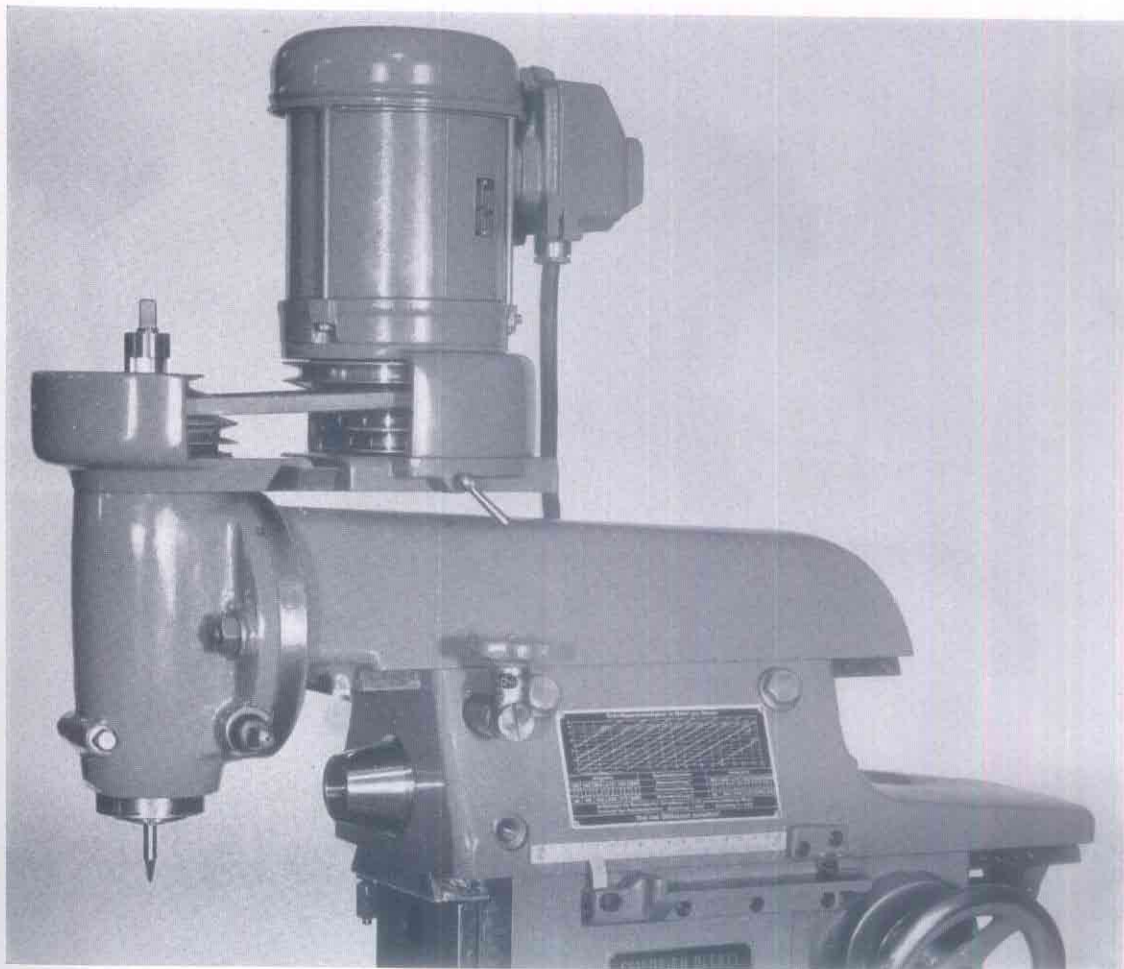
Schnellaufende Senkrechtfrässpindel FVVS
